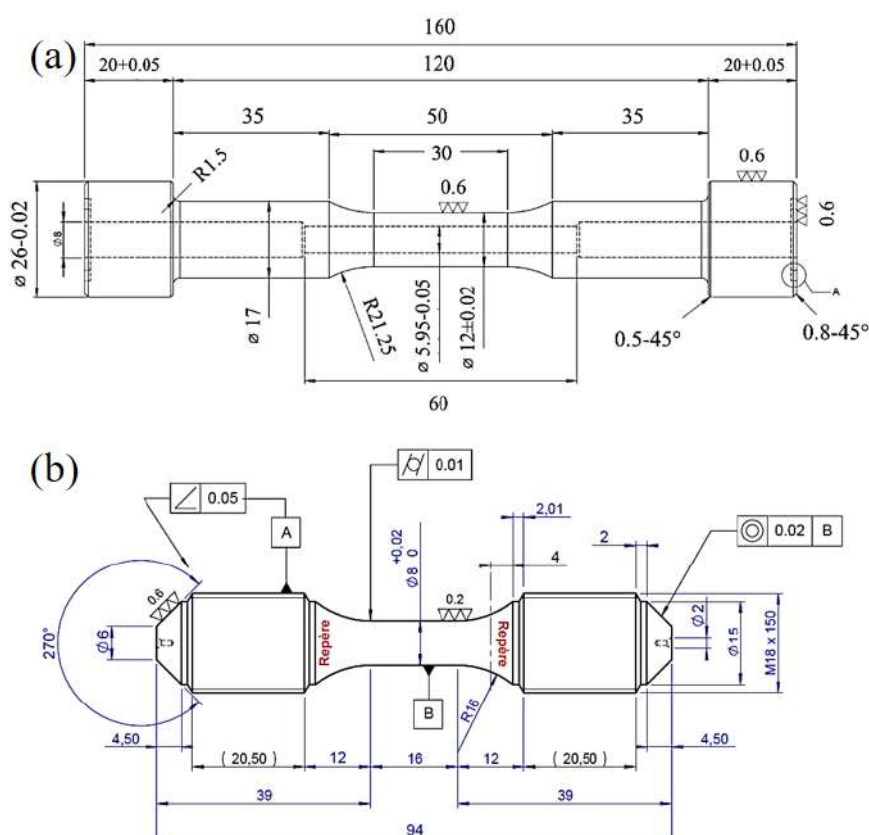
Géométrie des éprouvettes (en mm). (a) Éprouvettes tubulaires pour les essais en milieu REP et sous air à 300°C. (b) Éprouvettes cylindriques pour des essais complémentaires sous air à 300°C.
